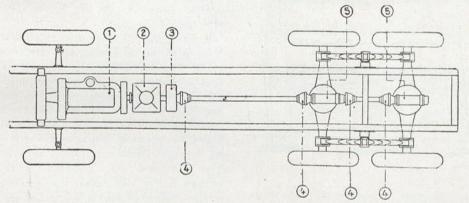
Planta de los chasis W. D.—1 Motor; 2 Cambio; 3 Reductor o demultiplicador; 4 Juntas de cardan; 5 Grupos de diferenciales.
